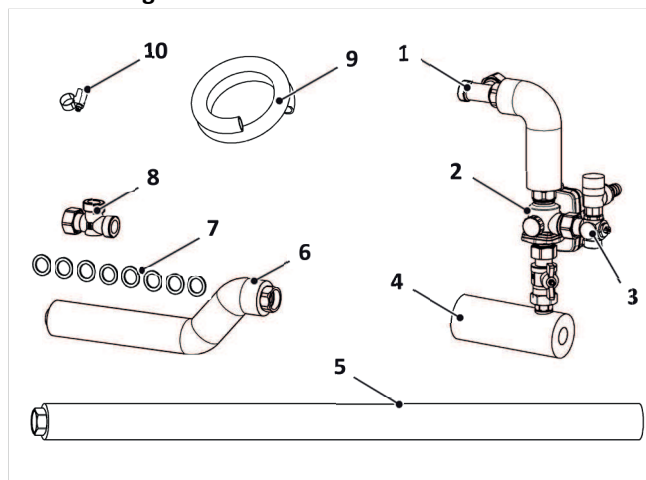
Montagepack LM WP / WP-SL 3-W Ventil
